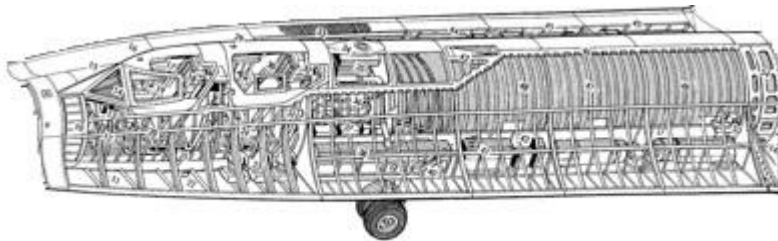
Parte delantera del fuselaje del Lockheed SR-71
